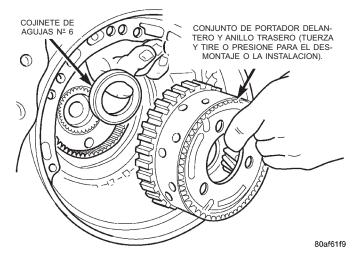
Desmontaje del conjunto de portador delantero y anillo trasero
